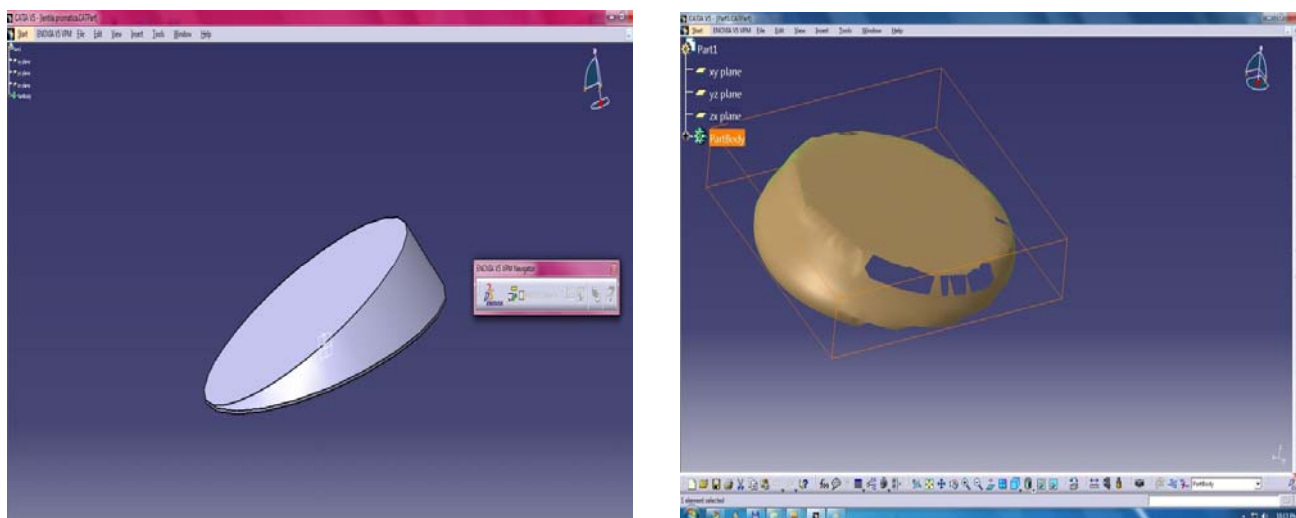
Forma geometrică constructivă a unei lentile prismatice: mediu CAD (stânga), scanare laser (dreapta).
